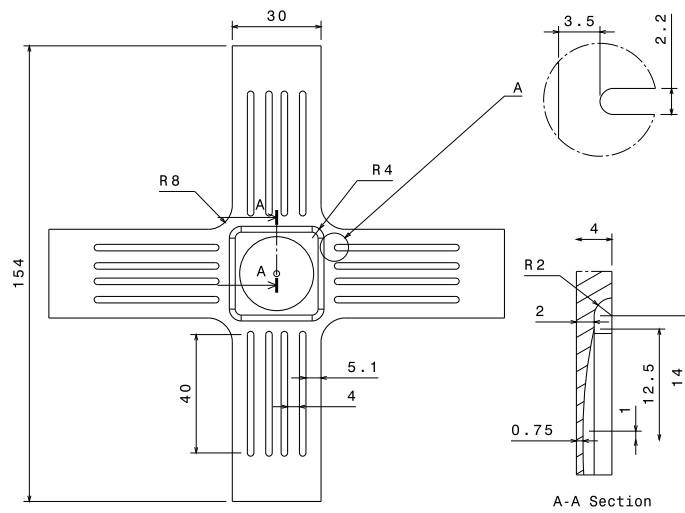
Géométrie de l'éprouvette optimisée.
